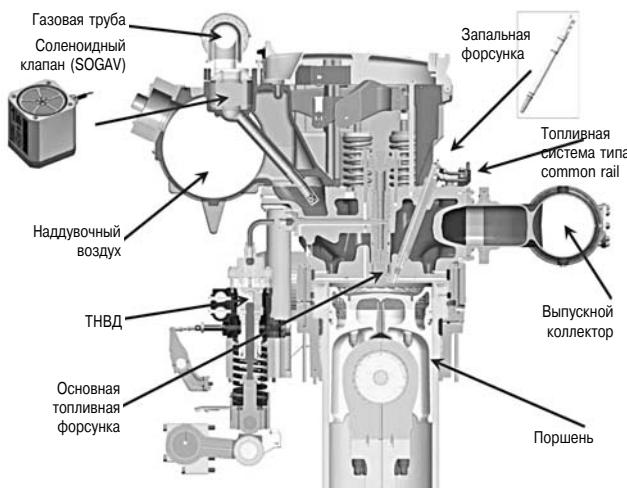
Конструкция системы подачи топлива в цилиндр дизеля фирмы «MAN Diesel & Turbo SE» типа DF
